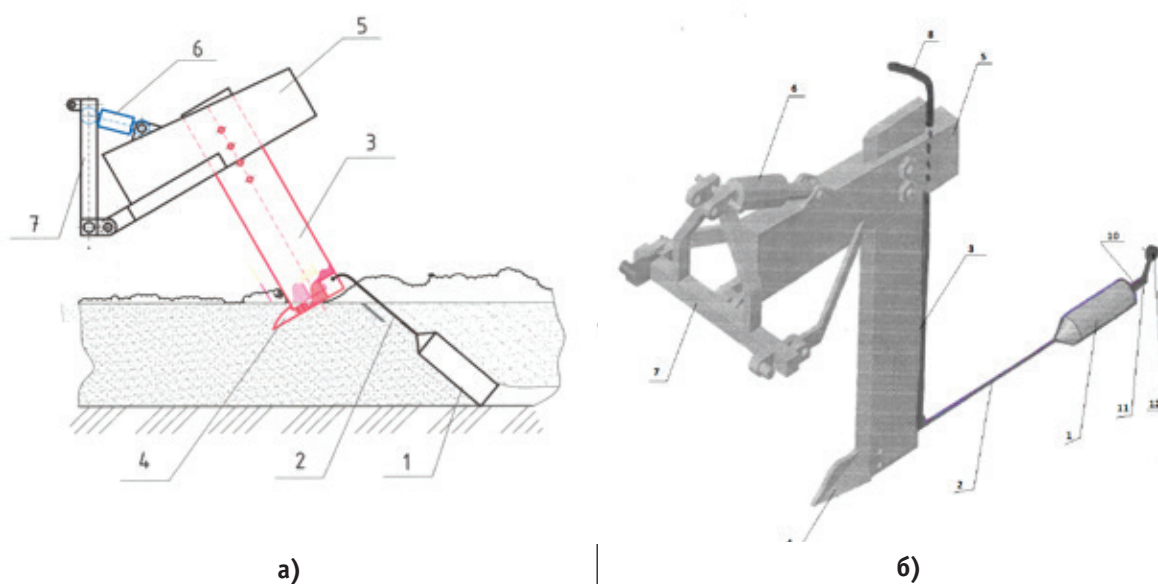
Дренажно-котовое орудие: а) схематический боковой вид навесного орудия; б) профильный вид навесного орудия. 1 — кротовой дренаж; 2 — трость; 3 — стойка; 4 — долото; 5 — подвижная рама; 6 — гидроцилиндр; 7 — неподвижная рама
